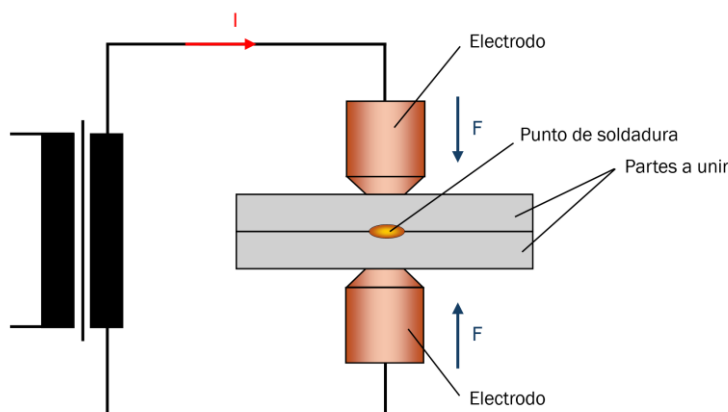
Representación esquemática del proceso de soldadura por puntos. Adaptado de [35]
